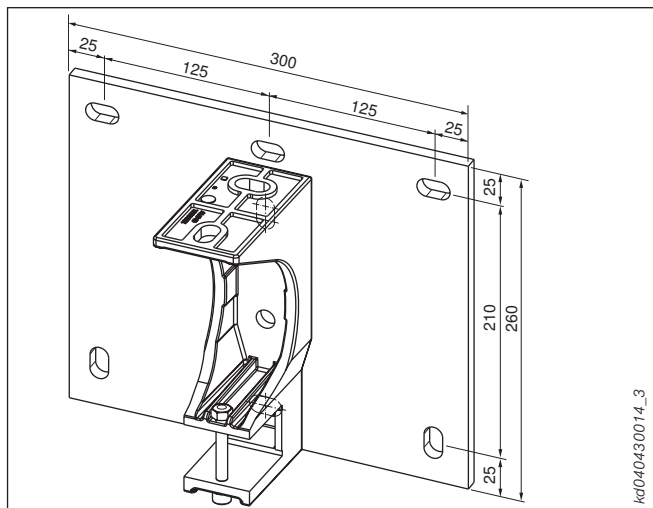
Consola tipo D – Fijación mural con placa de montaje grande
